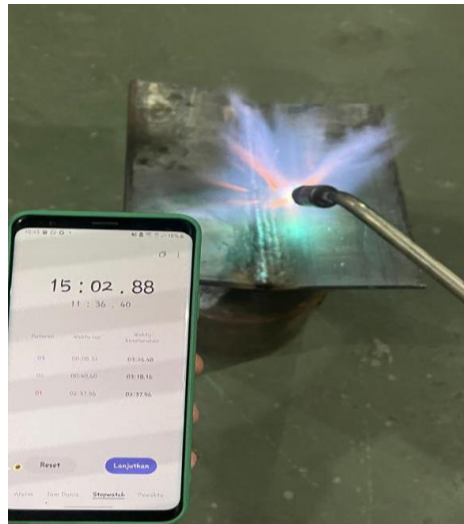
Flame straightening* pada *specimen* SMAW di suhu 400°C - 650°C
